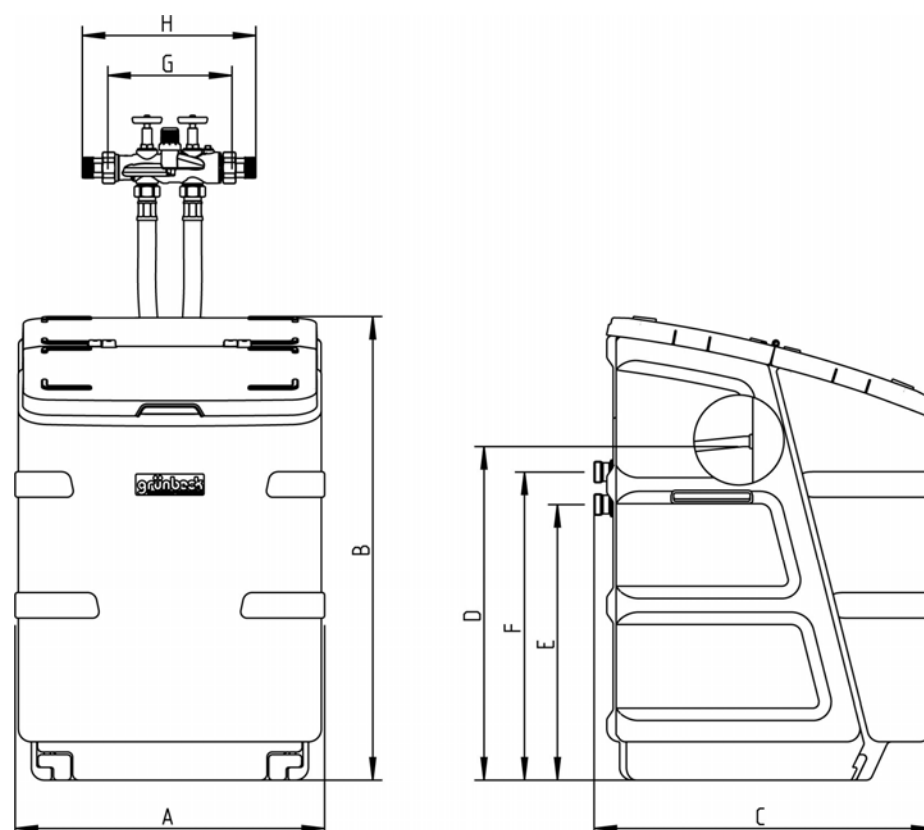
Plan coté du Weichwassermeister® GSX
